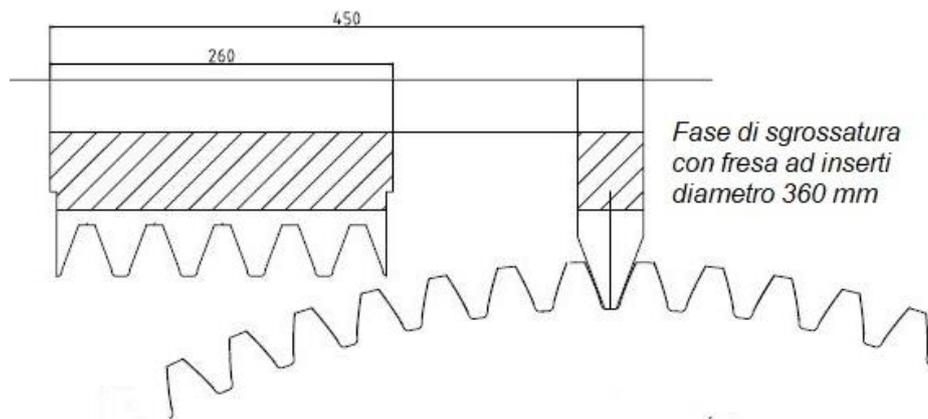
Schema di montaggio di fresa a sgrossare e di creatore integrale in HSS per la finitura
